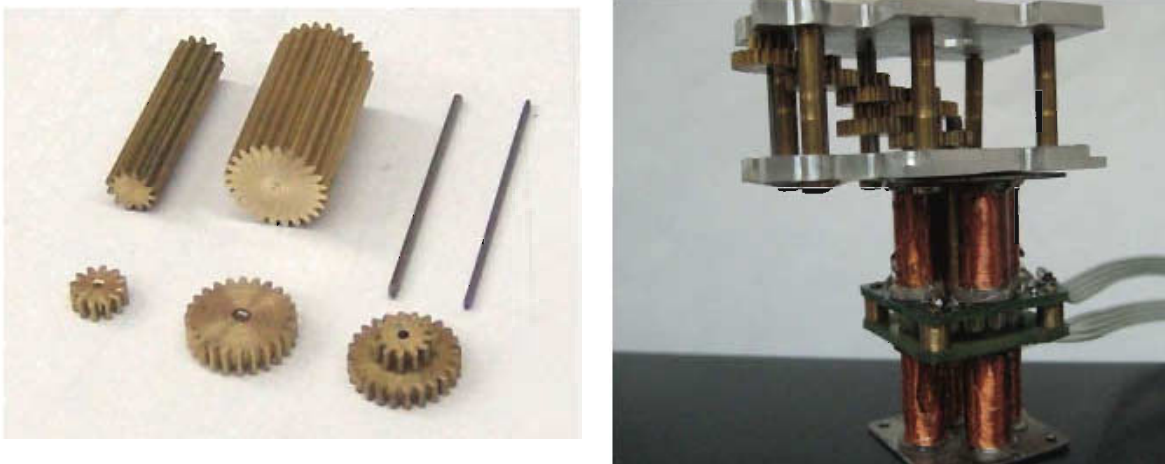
a) Juegos de engranes. b) Módulo de motor con reducción mecánica.
